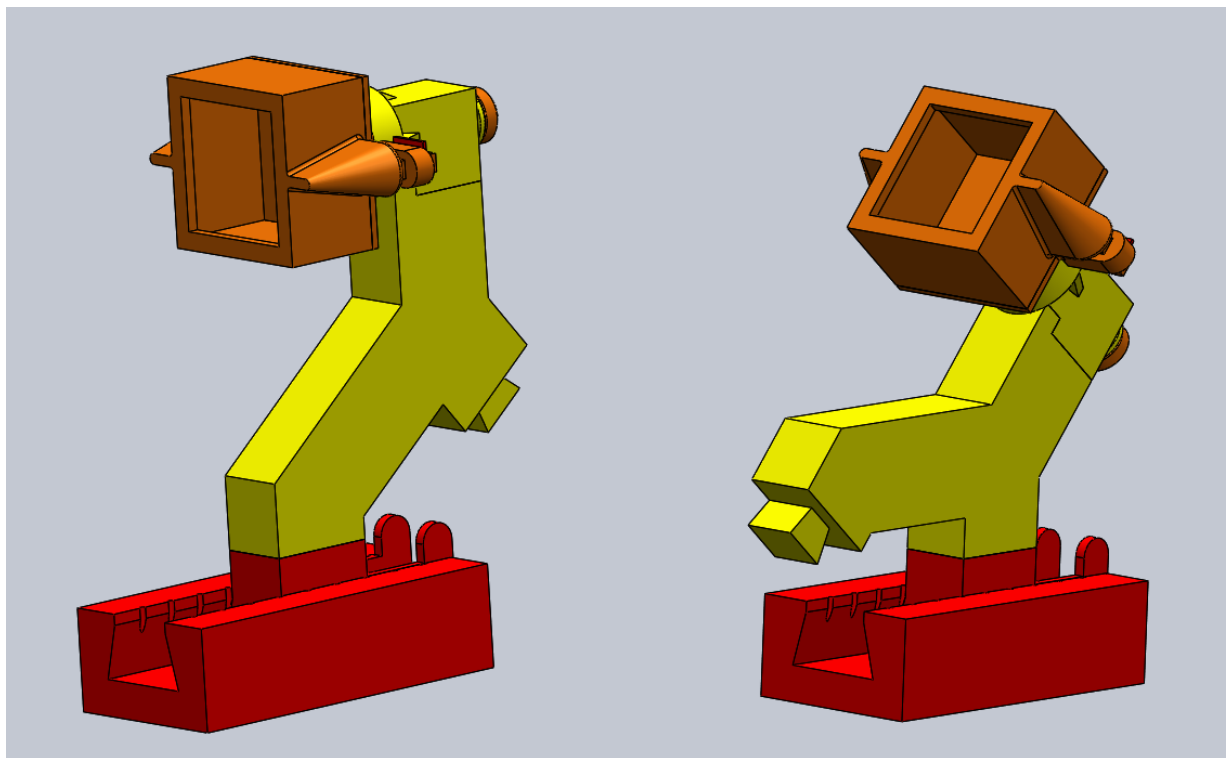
Perspectivas del ensamblaje terminado. A la izquierda: posición vertical. A la derecha: posición inclinado.
